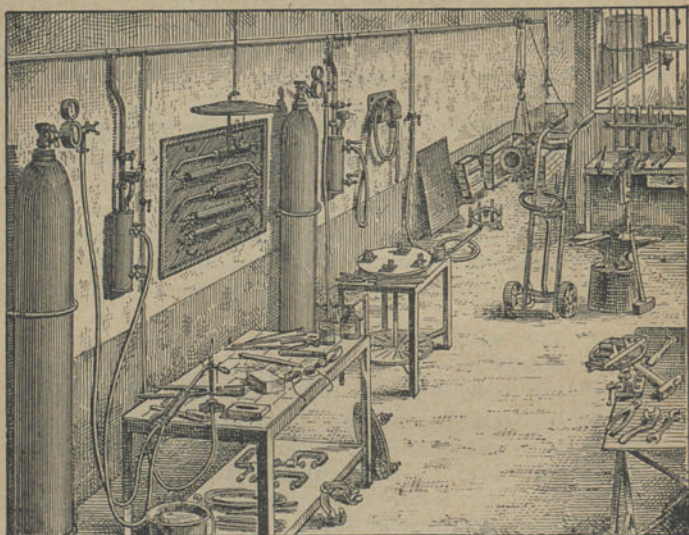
Os postos de soldadura numa instalação fixa.
